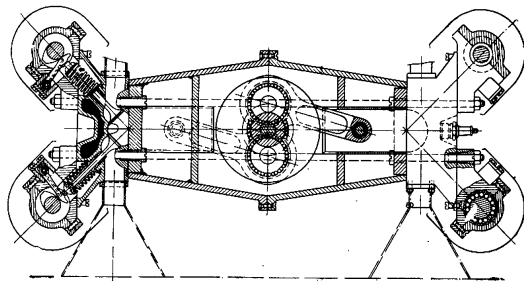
Чертеж поперечного разреза двигателя конструкции Грина
